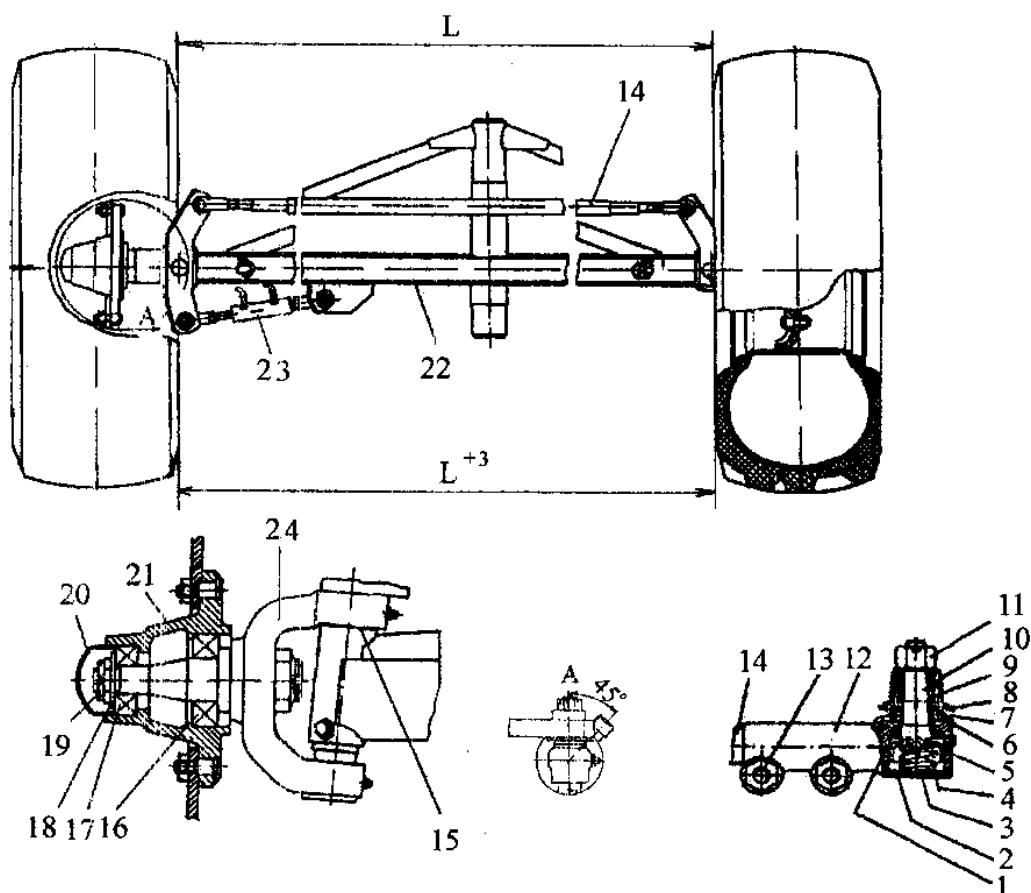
Мост управляемых колес: 1 – сухарь; 2 – заглушка; 3 – кольцо стопорное; 4 – пружина; 5 – пятак; 6 – обойма; 7 – уплотнитель; 8 – шайба защитная; 9 – рычаг; 10 – палец; 11, 13, 19 – гайки; 12 – наконечник; 14 – поперечная рулевая тяга; 15, 18 – шайбы; 16, 17 – подшипники; 20 – колпак; 21 – ступица; 22 – балка моста; 23 – гидроцилиндр; 24 – поворотный кулак; $L, L+3$ – размеры между колесами (схождение колес)
